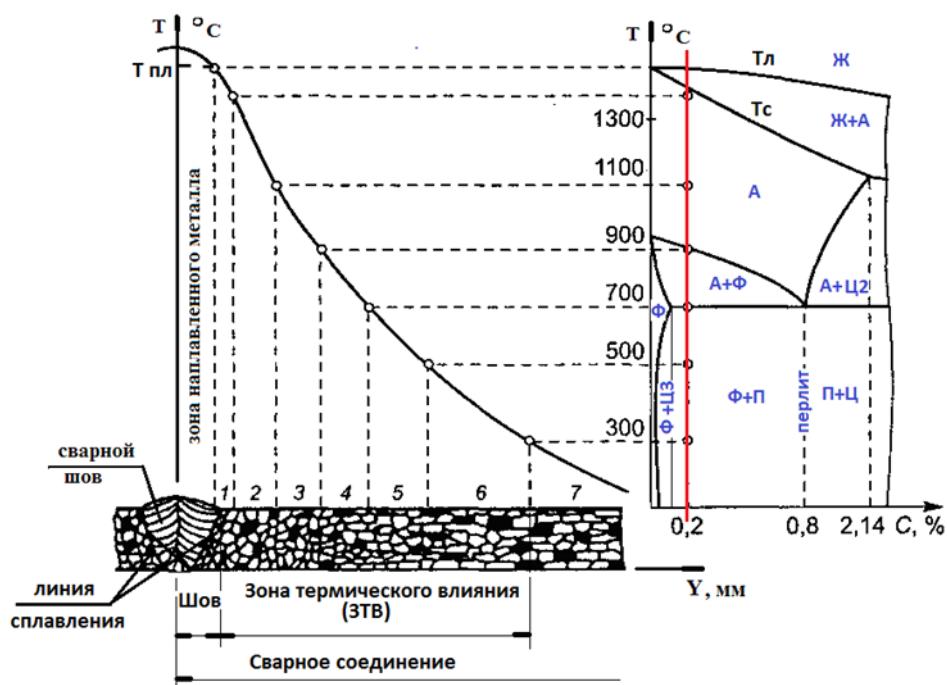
Схема строения зоны термического влияния сварного соединения при однослойной дуговой сварке низкоуглеродистой стали с
